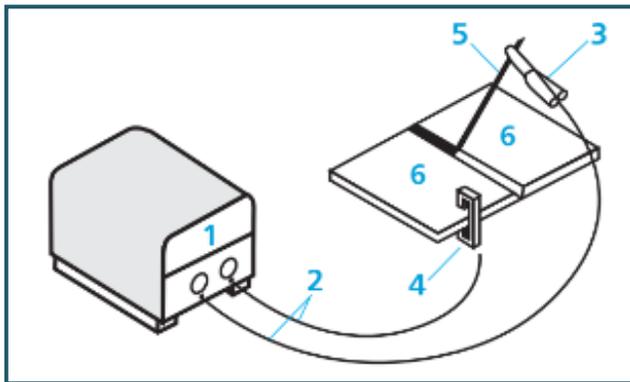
Partes del Circuito de Soldadura por Arco Eléctrico
